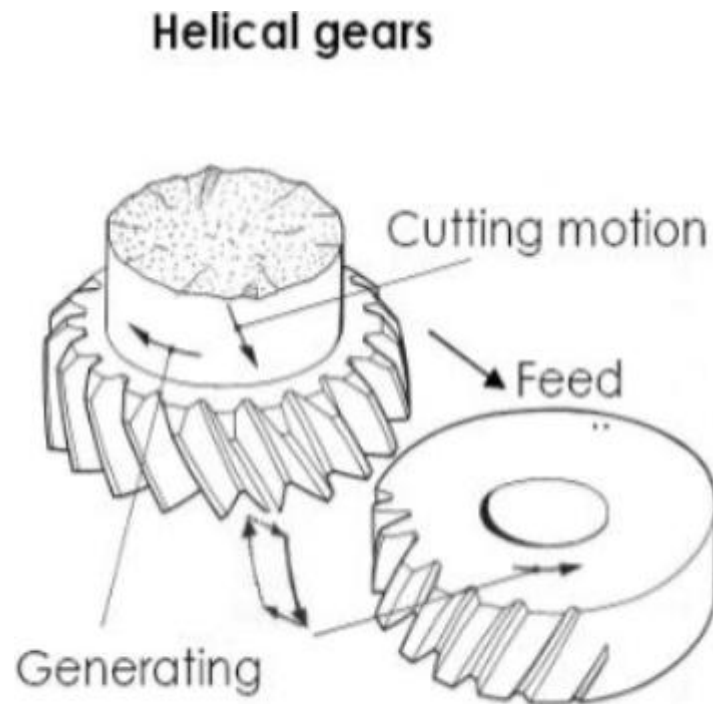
Зубонарізання косозубих коліс [5]
